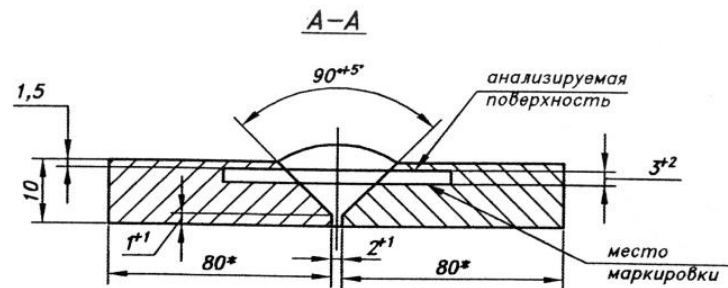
Схема вырезки заготовок для контроля проволоки перлитного класса под слоем флюса и электродов на ее основе и вырезки заготовок образцов из металла шва
